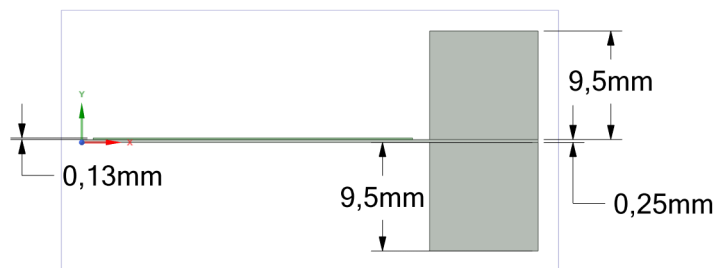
Modelo de placa plana com 16 rasgos e sem vigas
